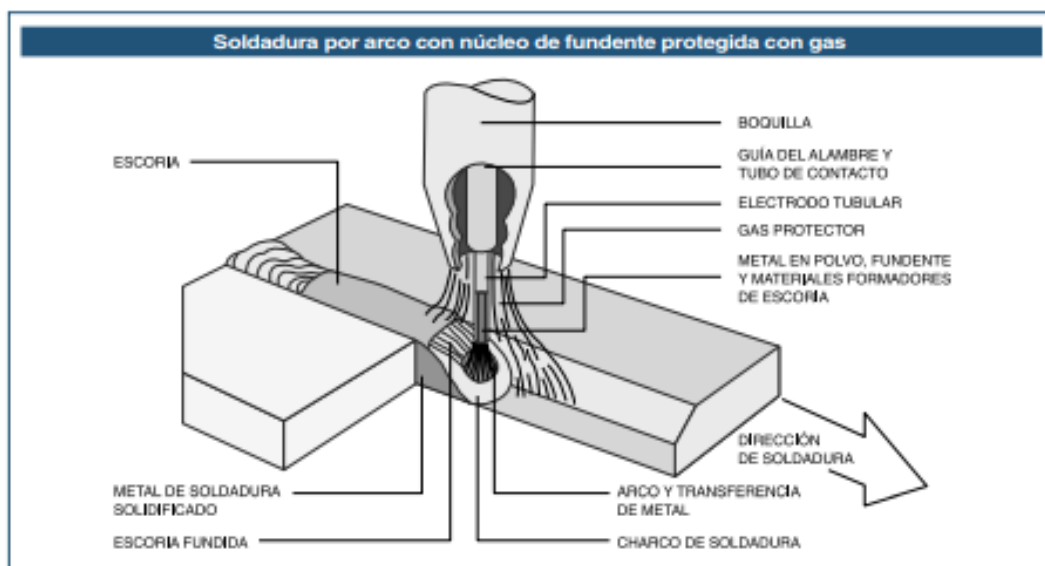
Soldadura eléctrica por arco bajo protección de gas con alimentación continua de electrodo tubular. (FCAW) [23].
